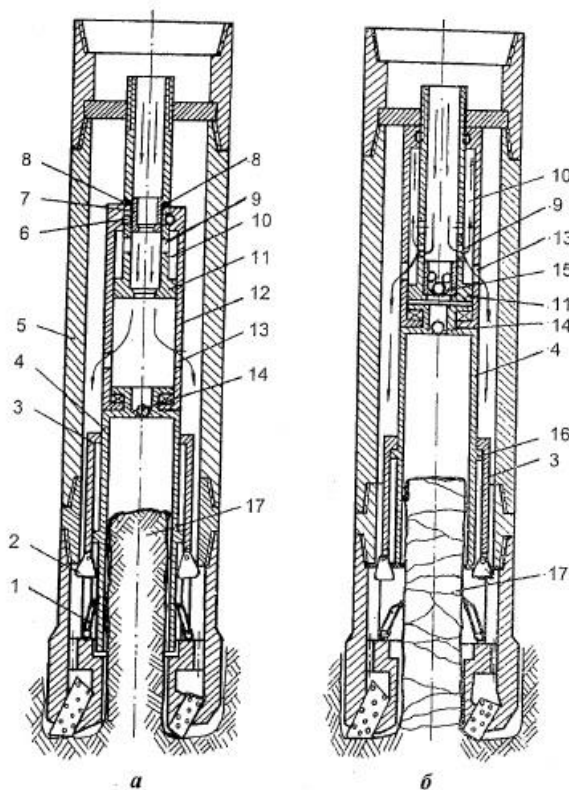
Схема двойного колонкового снаряда с подвижным (плавающим) керноприемником (ДКС-ПК-ТПИ): 1 – кернорвальный элемент клапанного типа; 2 – маятниковый фиксатор; 3 – корпус кернорвателя; 4 – керноприемная труба; 5 – наружная колонковая труба (корпус снаряда); 6 – замковый шарик-фиксатор; 7 – втулка; 8 – стопорная шпилька; 9 – отверстие в штоке поршня; 10 – камера давления жидкости; 11 – дно трубчатого поршня; 12 – корпус-цилиндр узла подвески; 13 – отверстие в корпусе узла подвески; 14 – нижний шаровой клапан; 15 – верхний шаровой клапан; 16 – кольцевой буртик корпуса кернорвателя, 17 – керн
